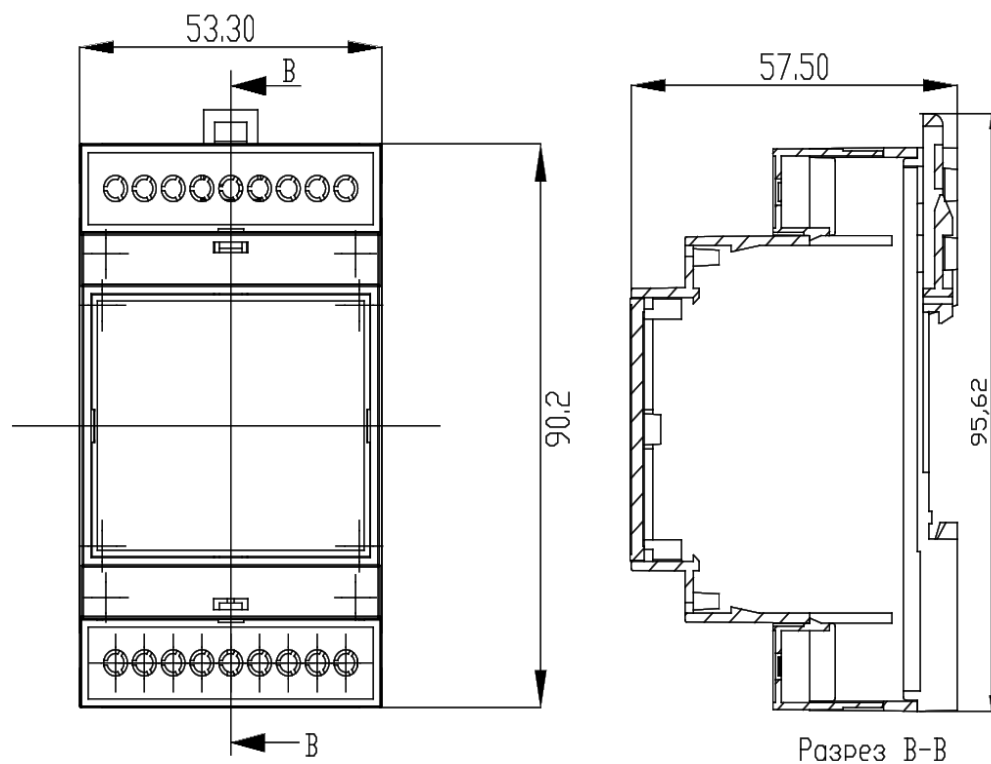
Габаритные размеры в малогабаритном корпусе.
